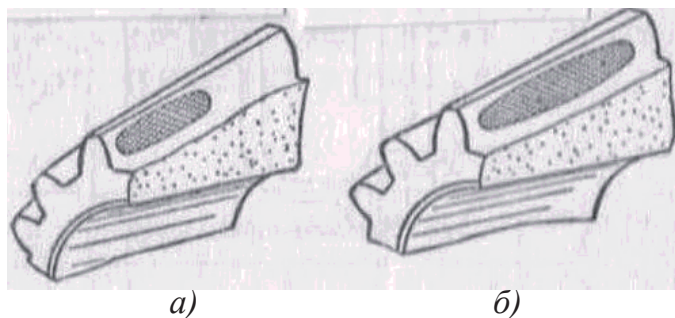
Расположение пятна контакта на боковой поверхности зуба конического колеса: а – при работе без нагрузки; б – при работе под нагрузкой
